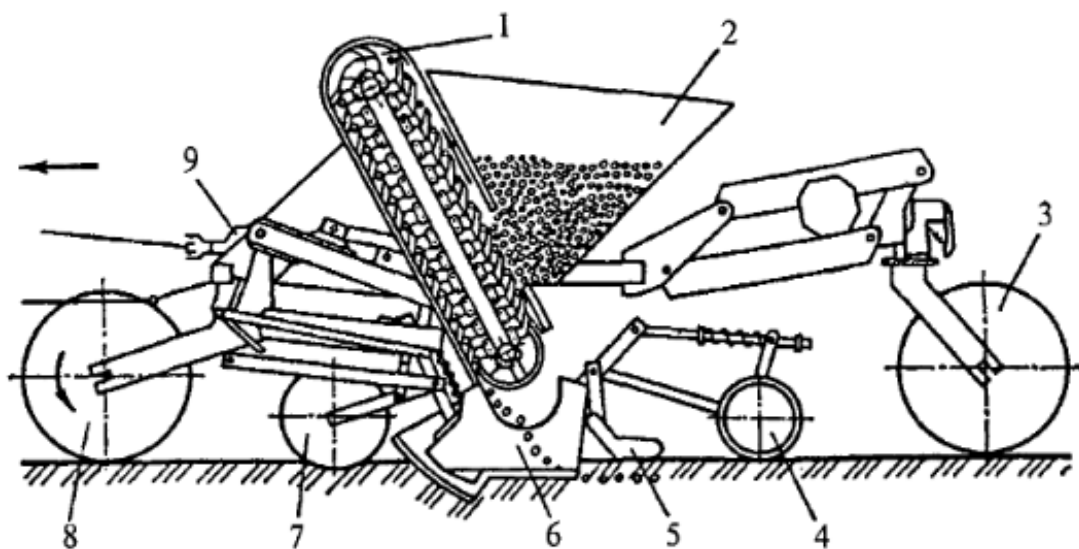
Функціональна схема сівалки ССС-4,2: 1 – висівний апарат; 2 – бункер для насіння; 3 і 8 – опорні колеса; 4 – коток прикотуючий; 5 – загортач; 6 – сошник; 7 – копіювальний коток; 9 – механізм приводу.
